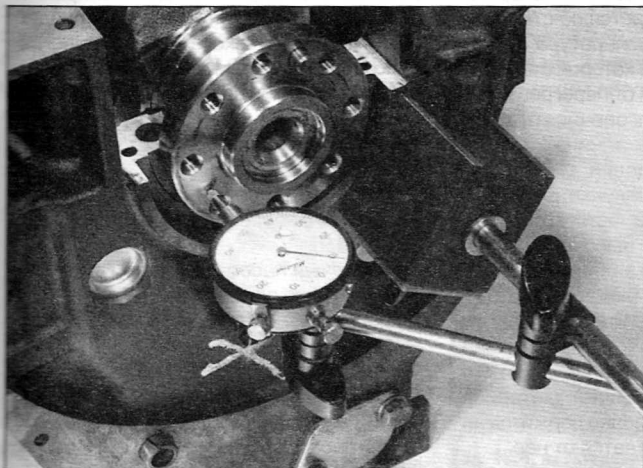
Проверка осевого зазора коленчатого вала с помощью стрелочного индикатора
